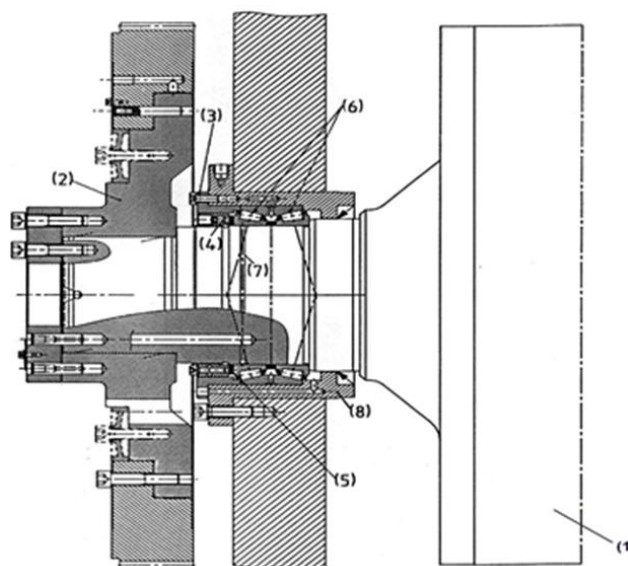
Конструкция опоры печатного цилиндра офсетной печатной машины Роланд 700 с коническими подшипниками:
